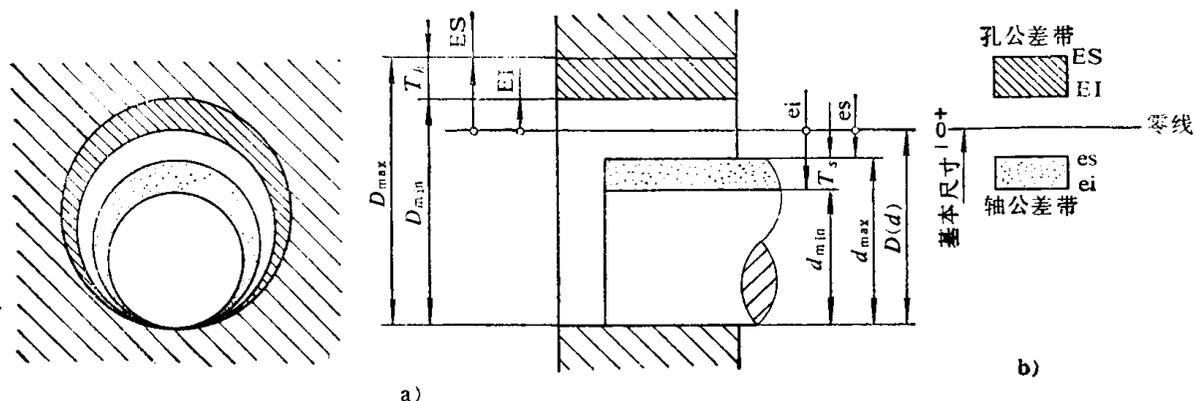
公差与配合的示意图和尺寸公差带图
